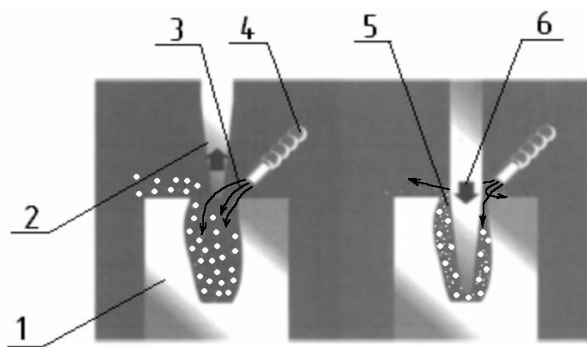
Влияние прокачки на эрозию заготовки: 1 – заготовка, 2 – электрод–инструмент, 3 – рабочая жидкость, 4 – насадка для подачи рабочей жидкости, 5 – эрозированные частицы, 6 – направление релаксации инструмента
